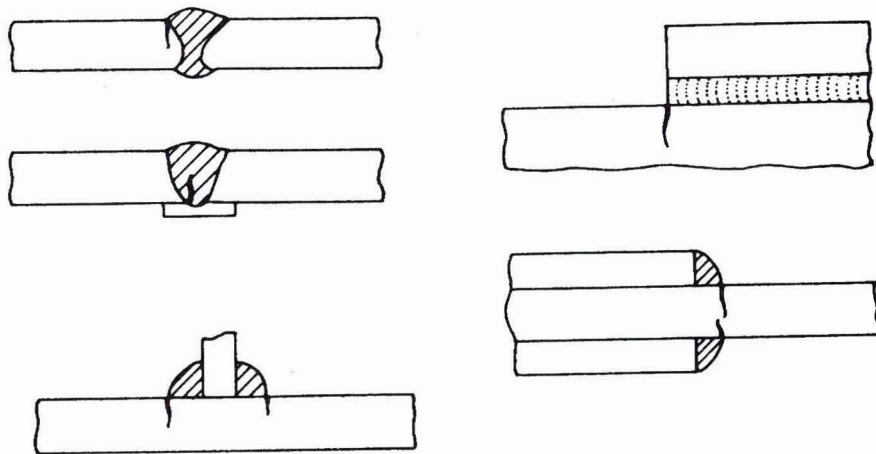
Zonas de uniones soldadas para la detección de grietas o roturas.
